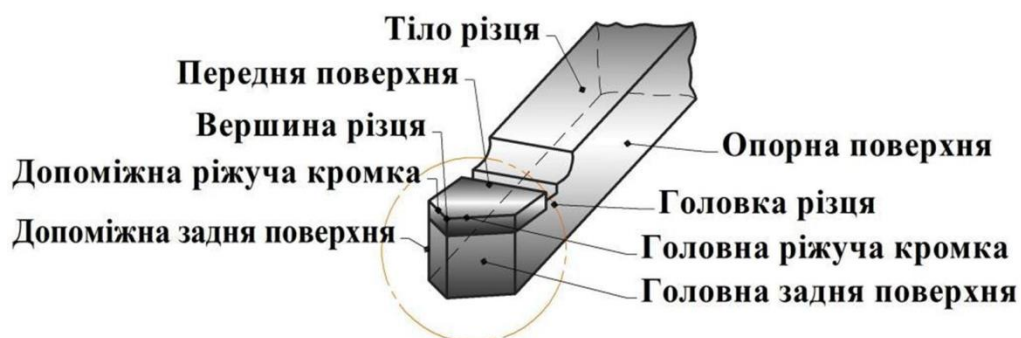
Робочі поверхні та ріжучі кромки різця
